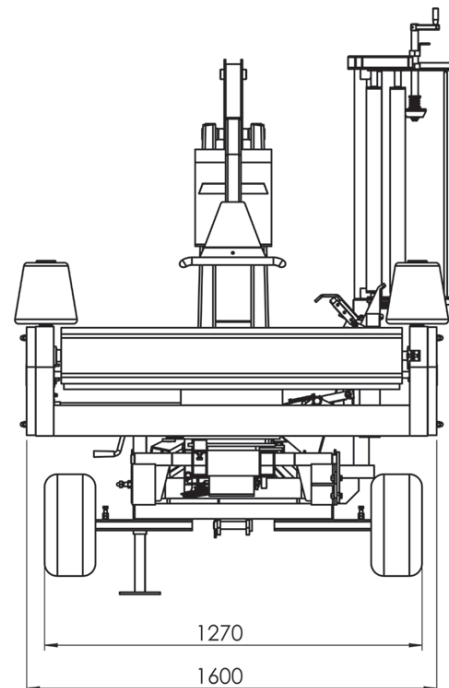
Dimensiones de la encintadora en la posición de transporte
